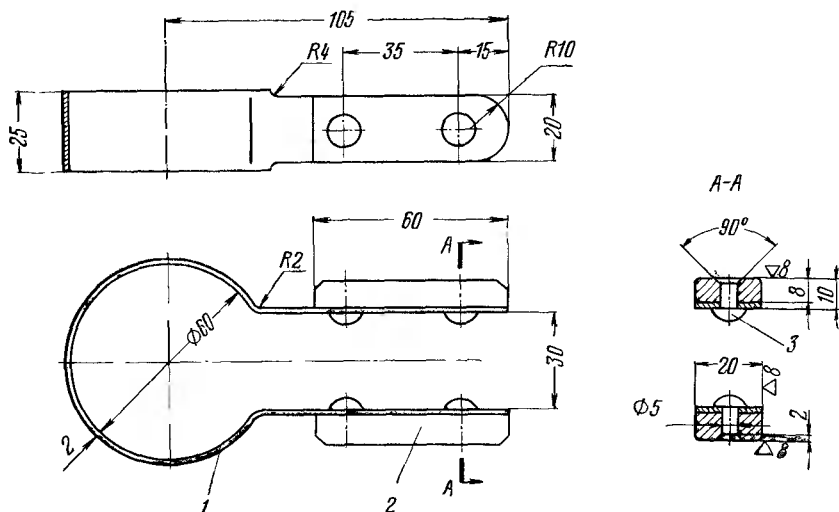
Обжимка для установки поршней в цилиндры компрессора:
